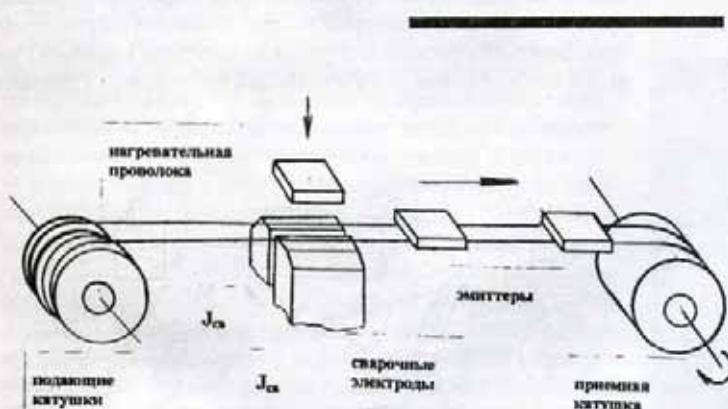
Кинематическая схема приварки проволочных нагревателей к эмиттеру
